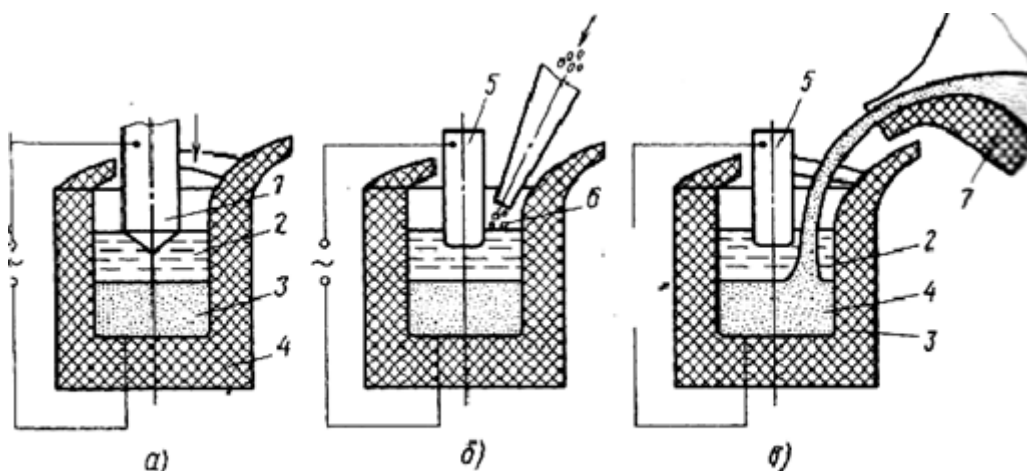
Схема приготовления жидкого металла в процессе электрошлаковой тигельной плавки:
